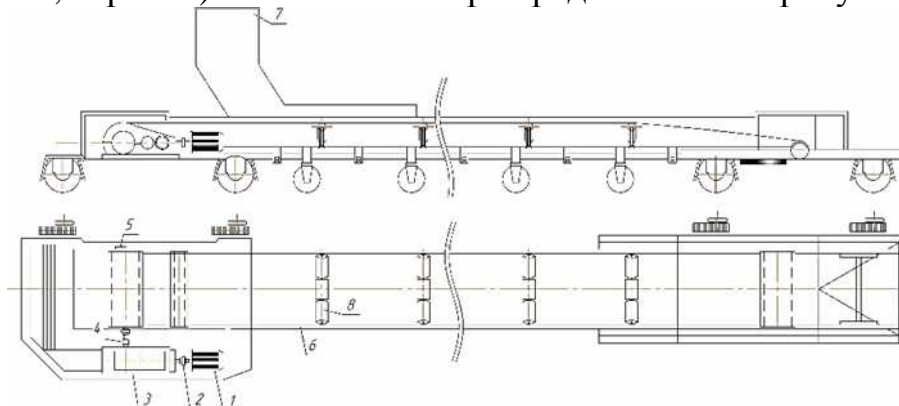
Общий вид конвейера: 1 – электродвигатель; 2 – муфта лепестковая; 3 – редуктор; 4 – муфта зубчатая; 5 – подшипник роlikовый сферический; 6 – лента конвейерная; 7 – погрузочное устройство; 8 – роlikоопора рабочей ветви
